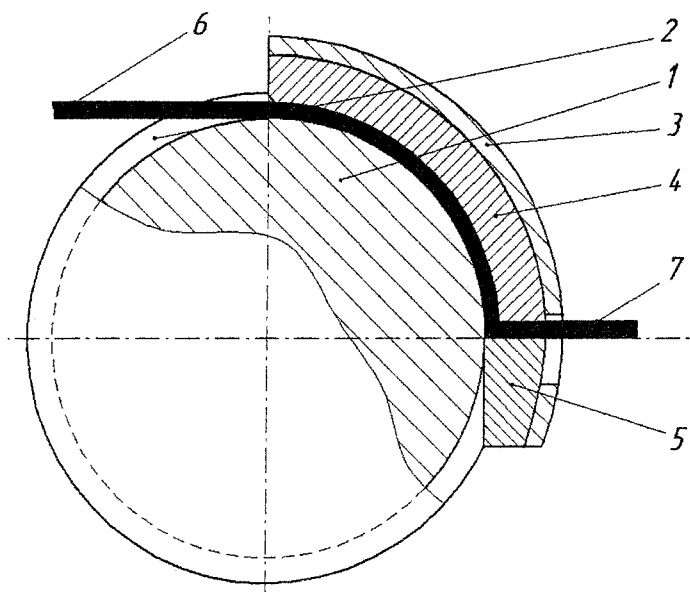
Схема процесса непрерывного прессования «Конформ»: 1 – рабочее колесо; 2 – П-образная канавка; 3 – башмак; 4 – кольцевая вставка; 5 – упор; 6 – заготовка; 7 – изделие
